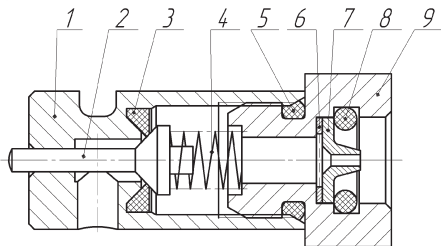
Схема механизмов pistols MP-651K, MP-651K
